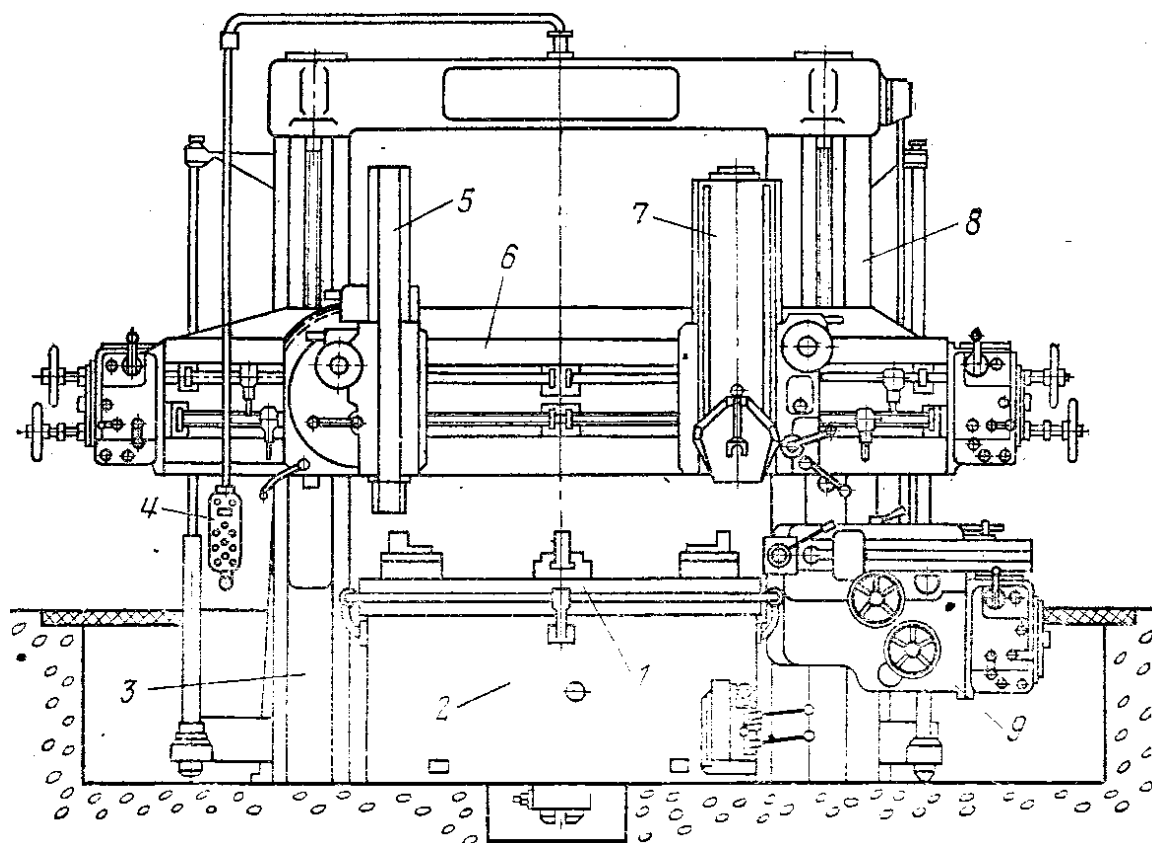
Загальний вигляд токарно-карусельного верстату
